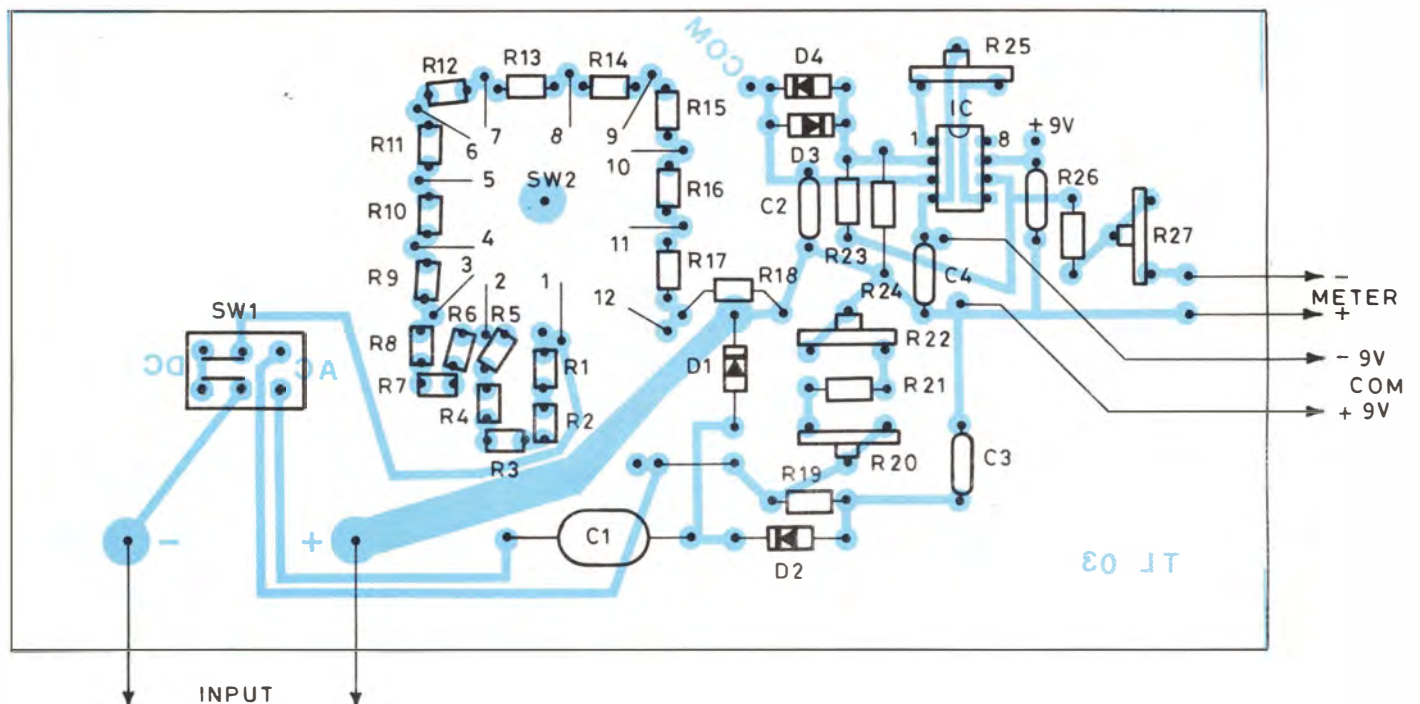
Disposizione dei componenti sul circuito stampato di fig. 4
